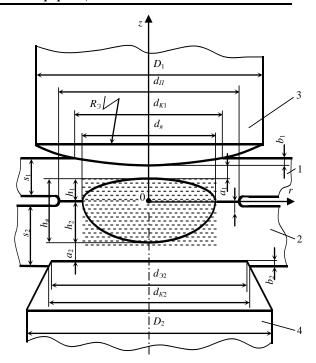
Схема геометрических параметров точечного сварного соединения деталей 1 и 2 разных толщин (при КТС с использованием электродов со сферической 3 или плоской 4 рабочими поверхностями)
